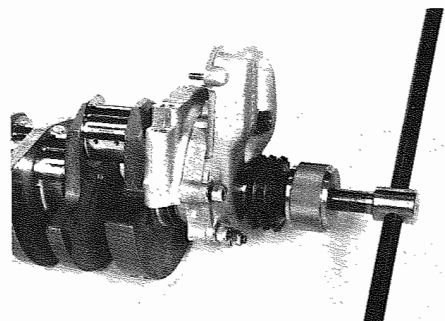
Smontare il pignone distribuzione e la pompa olio
